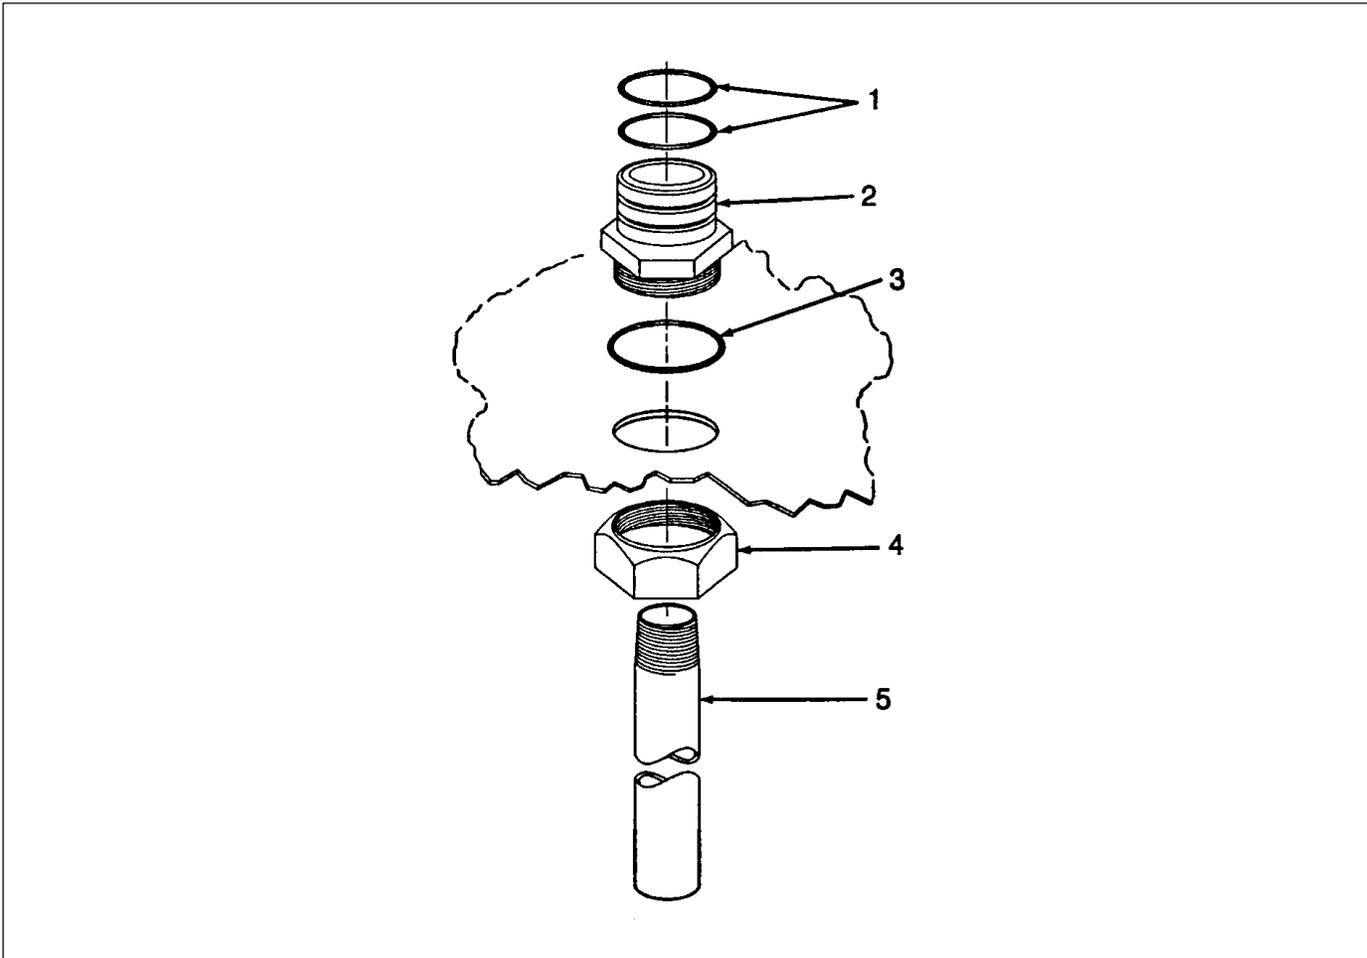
Kit de montaje (142 063 & 142 632)
